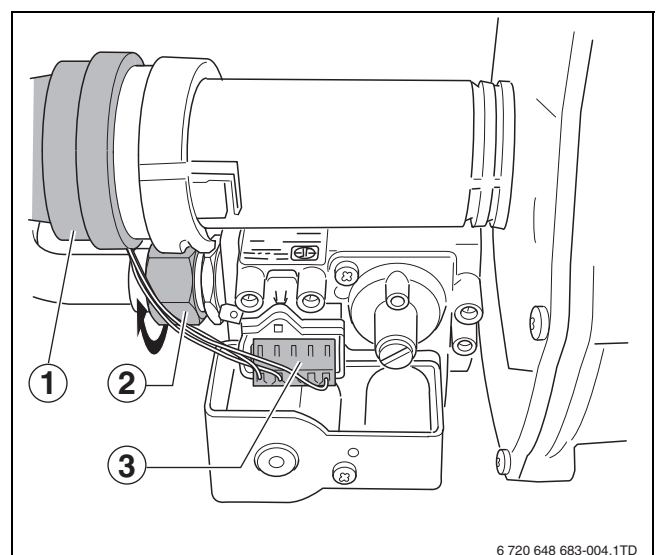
Smontaggio del tubo di aspirazione dell'aria, della spina di alimentazione elettrica e del dado di raccordo
